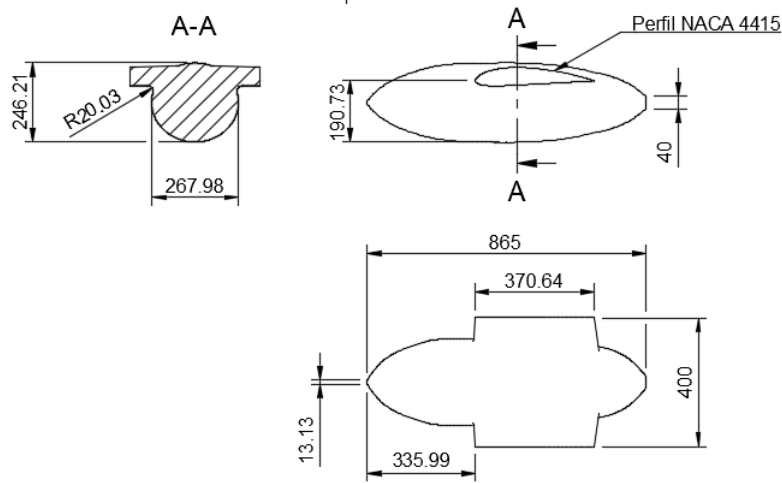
Dimensiones generales del fuselaje (dimensiones en mm).
